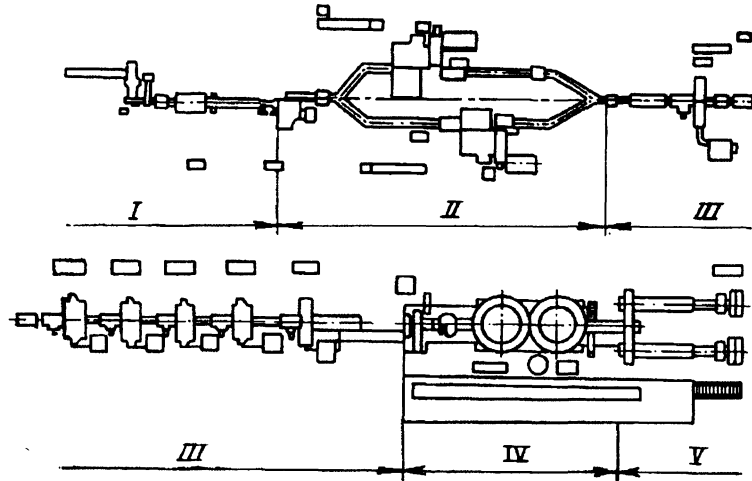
Линия сварки колес легкового автомобиля с участками:
